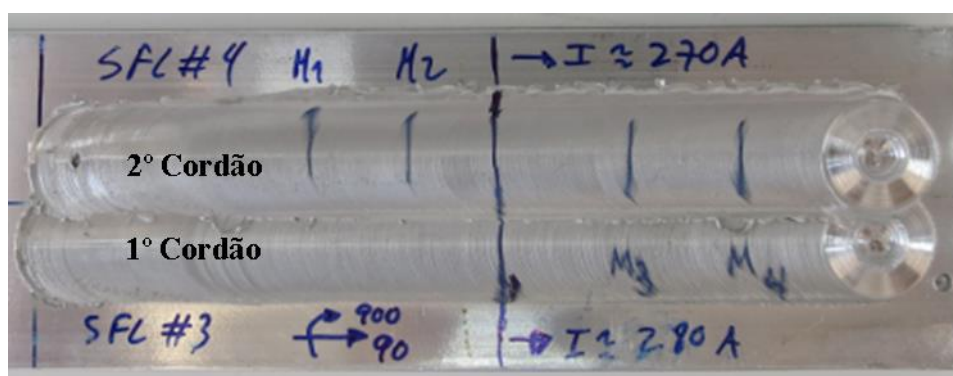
Esquema de cordões na soldadura de juntas sobrepostas.
